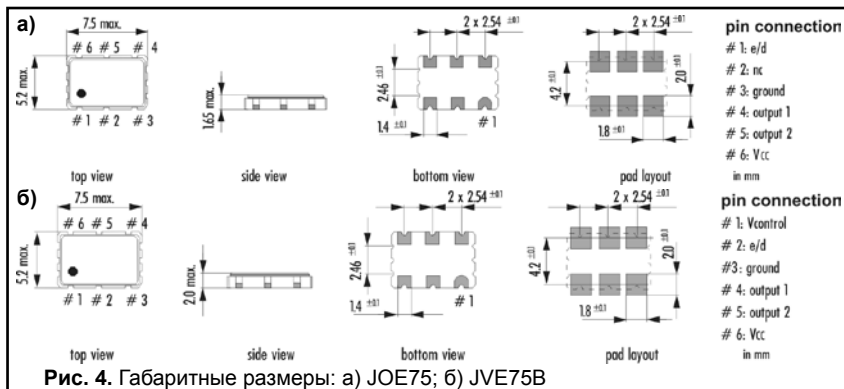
Габаритные размеры: а) JOE75; б) JVE75B
